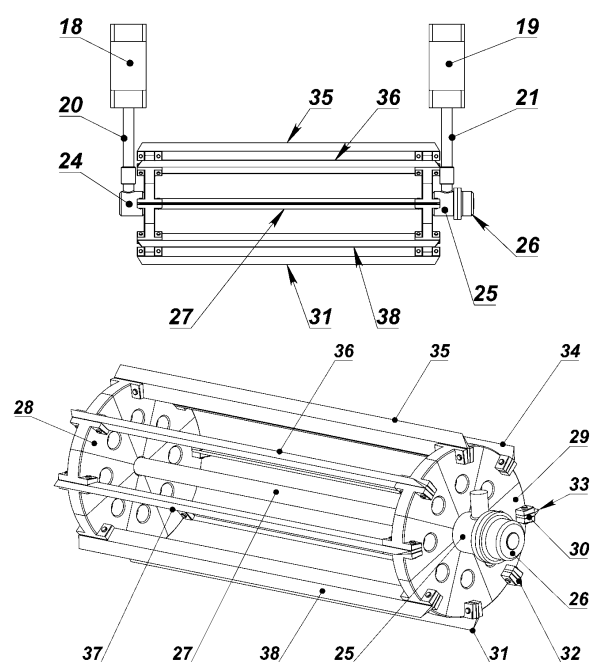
Машина для резки рыбы на ломтики. Ротор со сменными ножами
